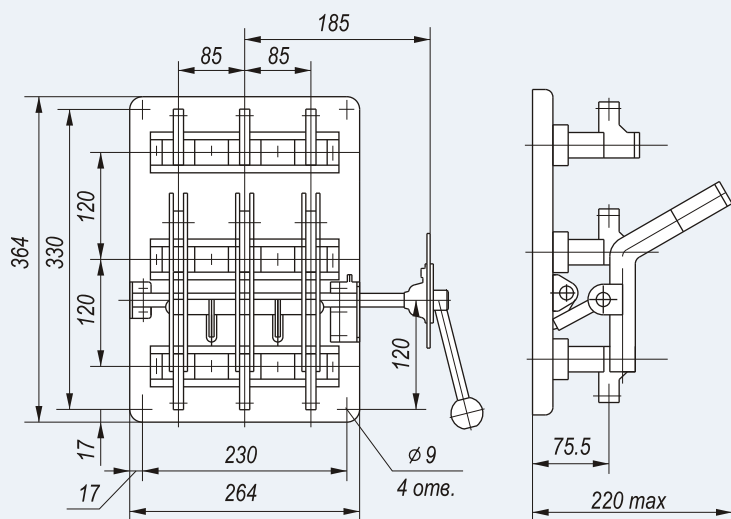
Переключатель с боковой рукояткой ПБ-2, ПБ-4
